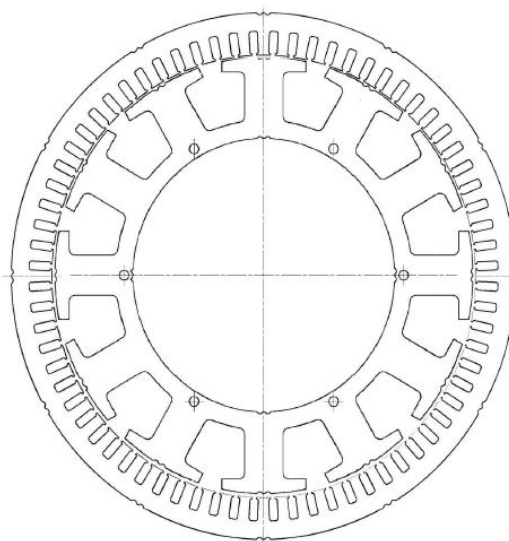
Machine à rotor bobiné et à pôles saillants - Alerno-démarrreur Valeo-LEC
